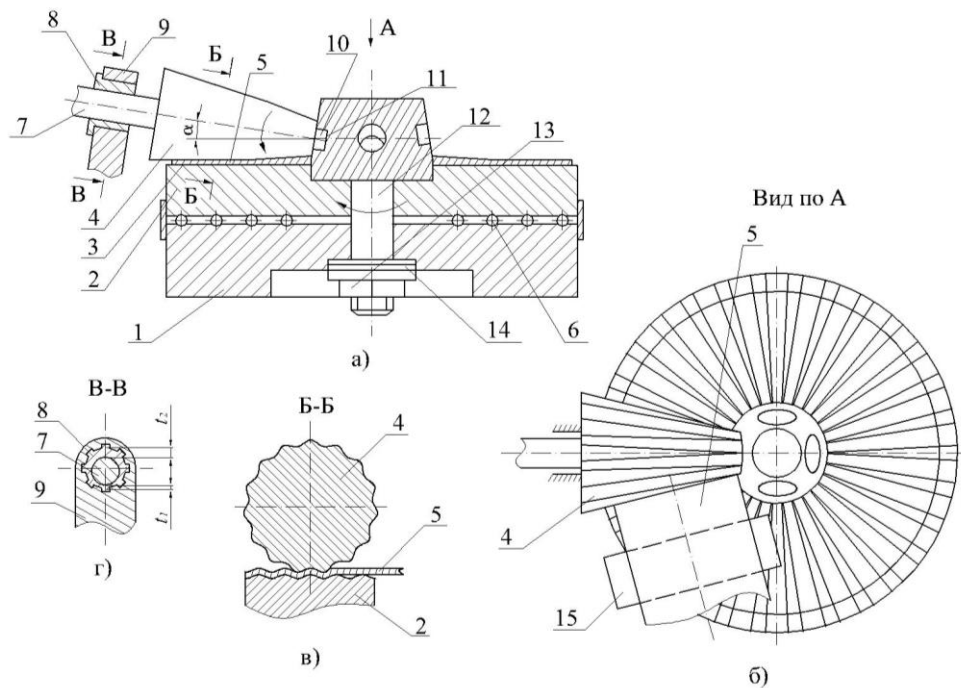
Пристрій для виготовлення гофрованих гвинтових заготовок конічними формуючими елементами:
